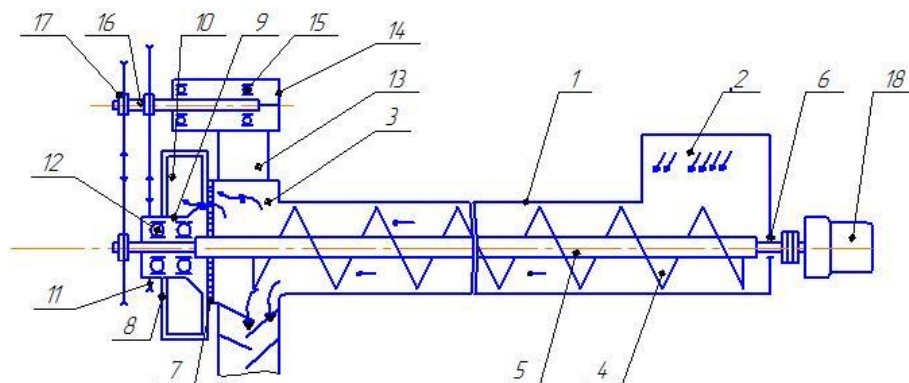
Схема пневмовинтовой установки с устройством для удаления легких примесей: 1 - кожух, 2 - загрузочное устройство, 3 - разгрузочное устройство, 4 - шнек, 5 - вал, 6 - задняя опора, 7 - перфорированная стенка, 8 - кожух вентилятора, 9 – стакан, 10 - лопасти, 11, 17 - ременная передача, 12,15 - подшипники, 13 - кронштейн, 14 – обойма, 16 - контрприводной вал, 18 – привод.
